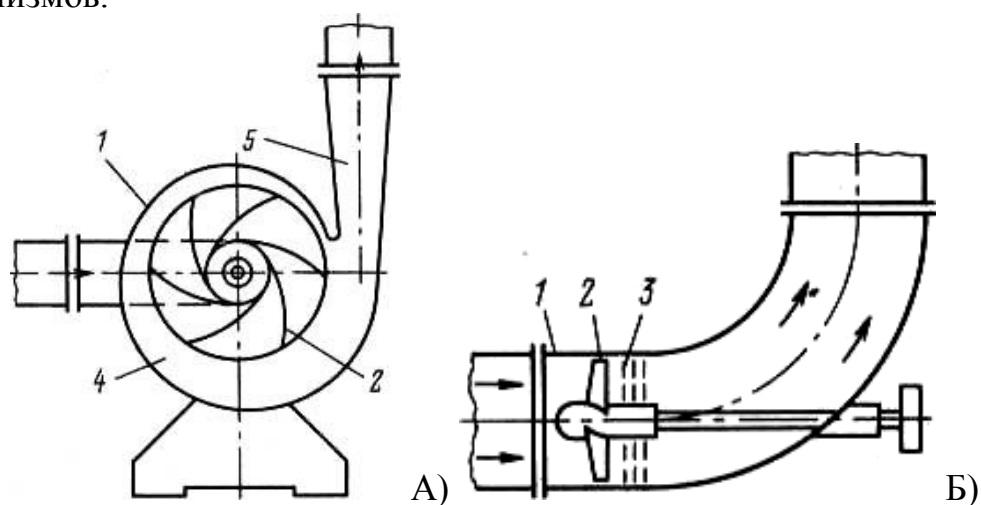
Конструктивные схемы механизмов центробежного А) и осевого Б) типов: 1-корпус; 2-лопасти; 3- направляющий аппарат; 4-спиральный отвод; 5-напорный патрубок.
